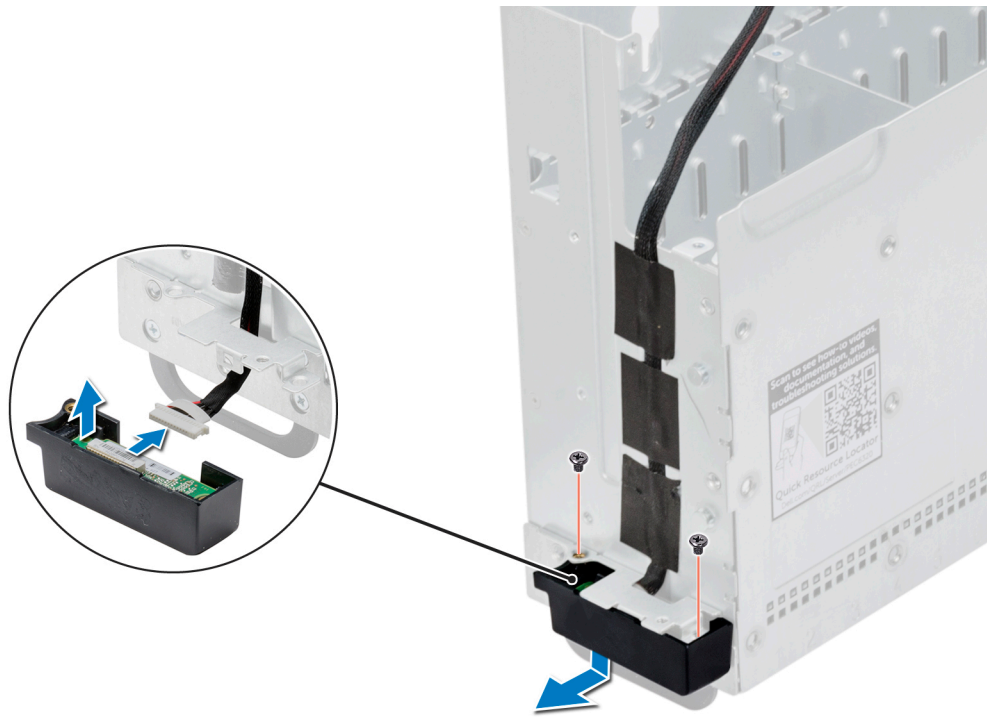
Retrait de l'assemblage du panneau de commandes gauche
